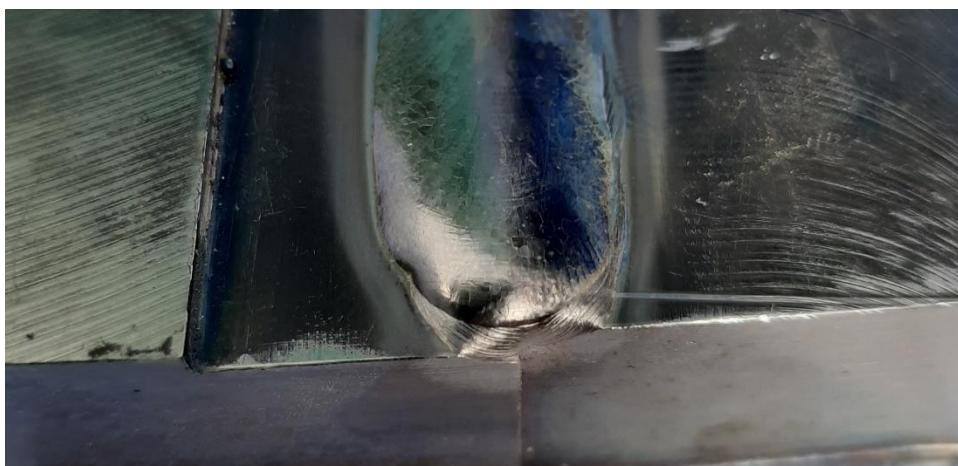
Сварное соединение титановых плит марки ВТ6ч
